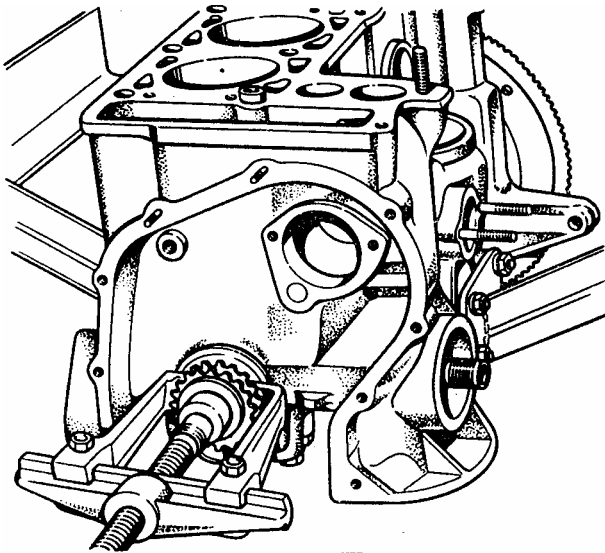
Remoción de la estrella del cigüeñal con ayuda del extractor universal A.40005/1/7
